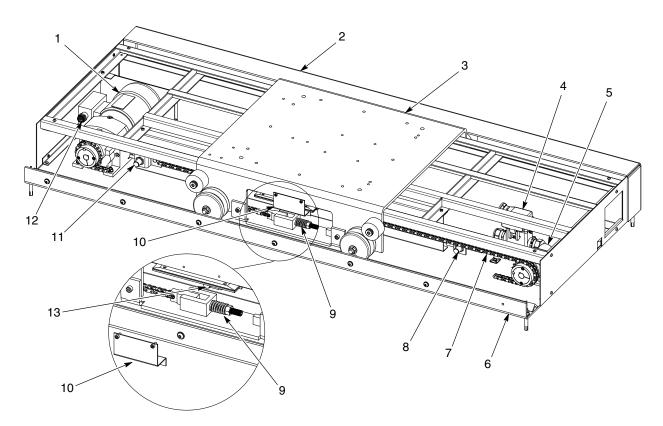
Componentes del posicionador (se muestra sin cable guía)
